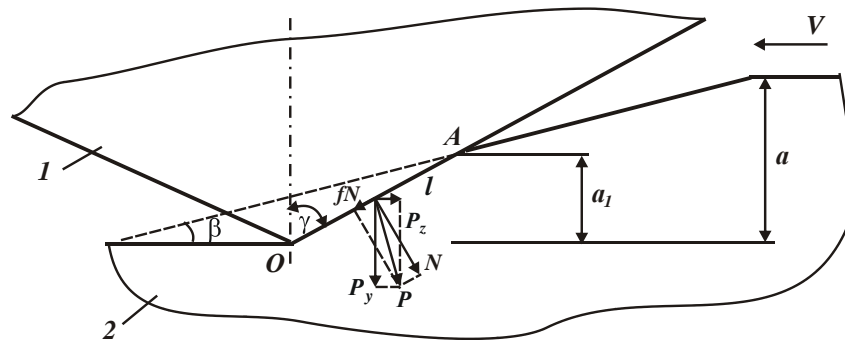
Расчетная схема резания: 1 – резец; 2 – обрабатываемый материал
